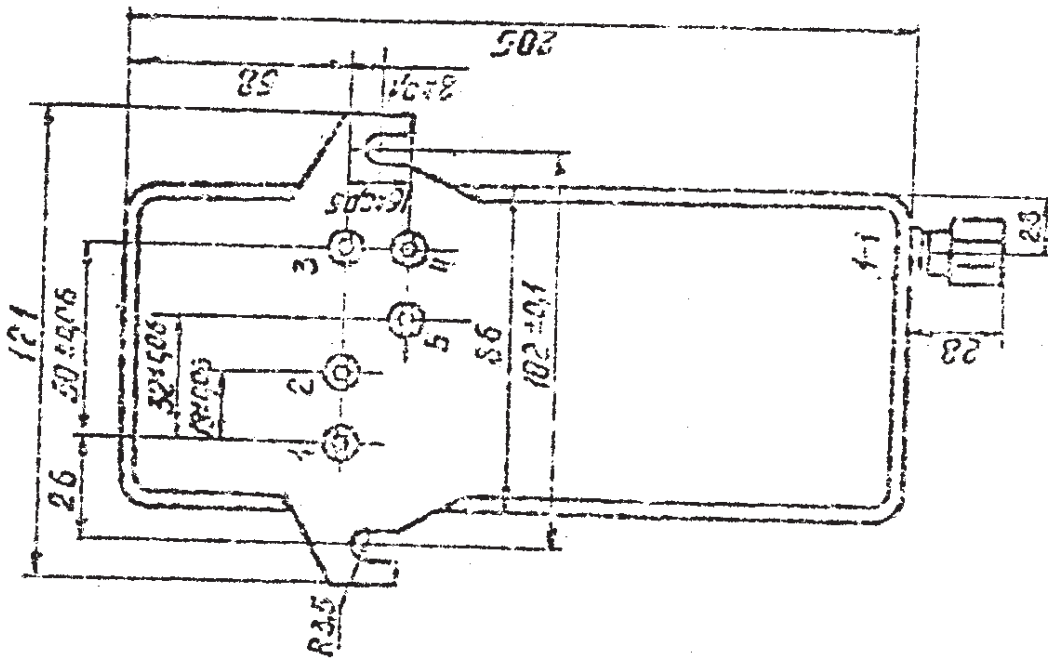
Габаритные, установочные и присоединительные размеры регулятора ПР3.53-М1
